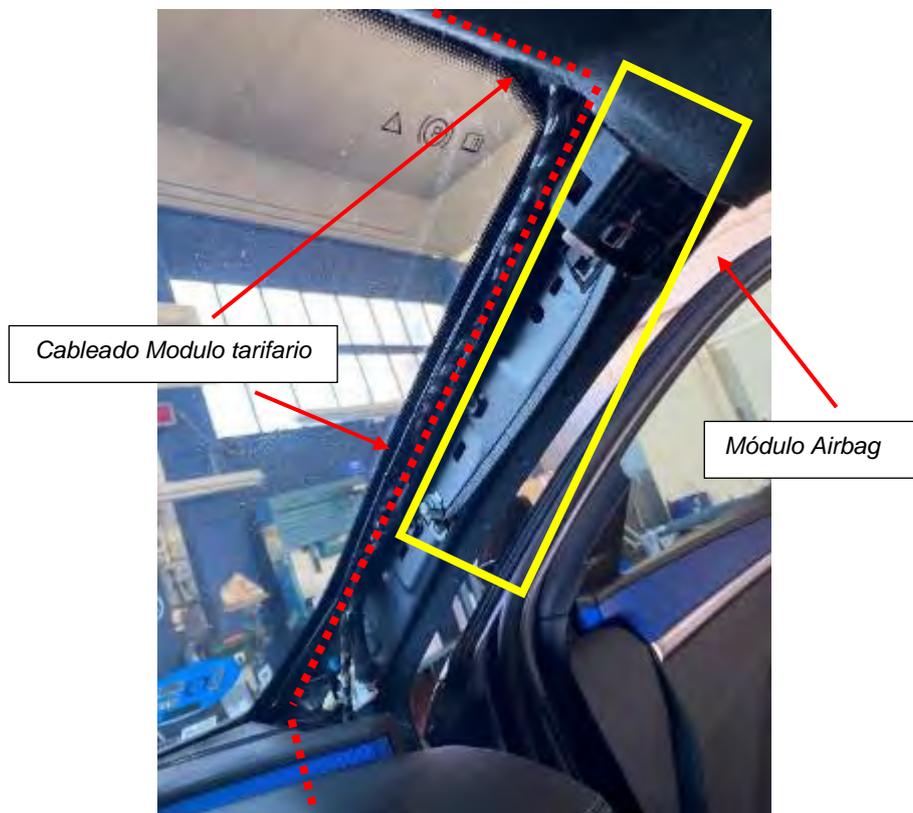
Recorrido del cableado a traves del pilar A.
